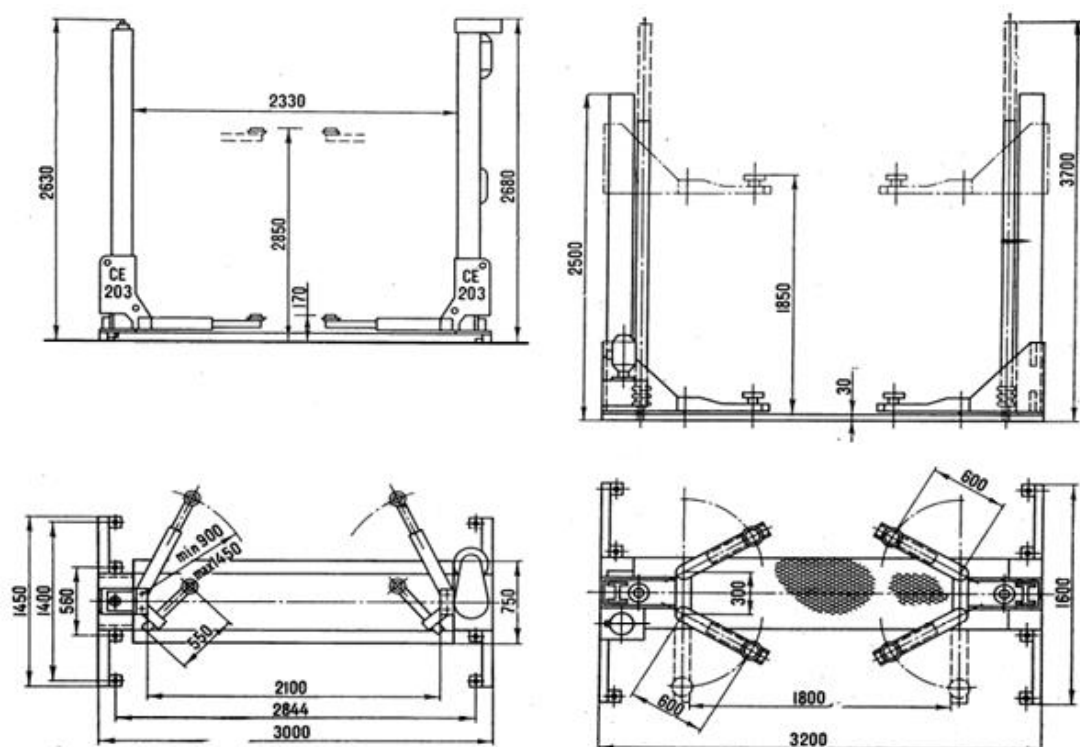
Двохопорний вилочний підйомник CE-203 та ZFA-321
